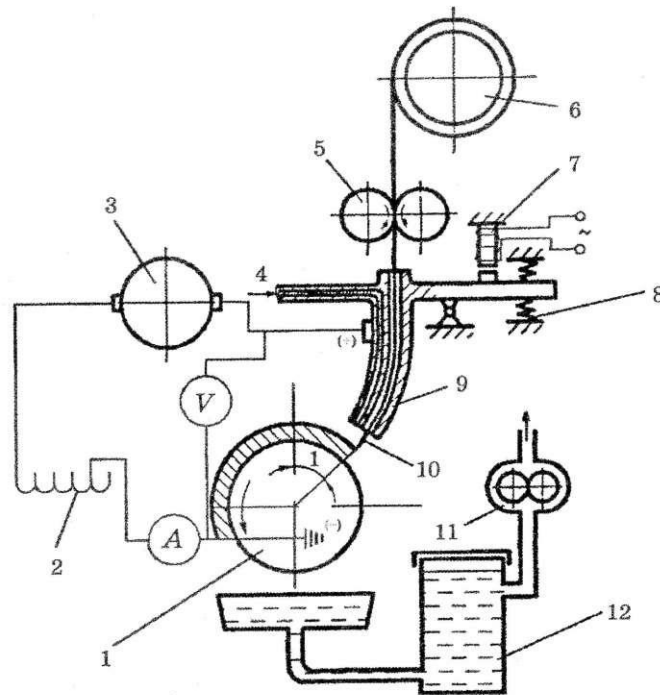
Схема установки для вібродугового наплавлення деталей
